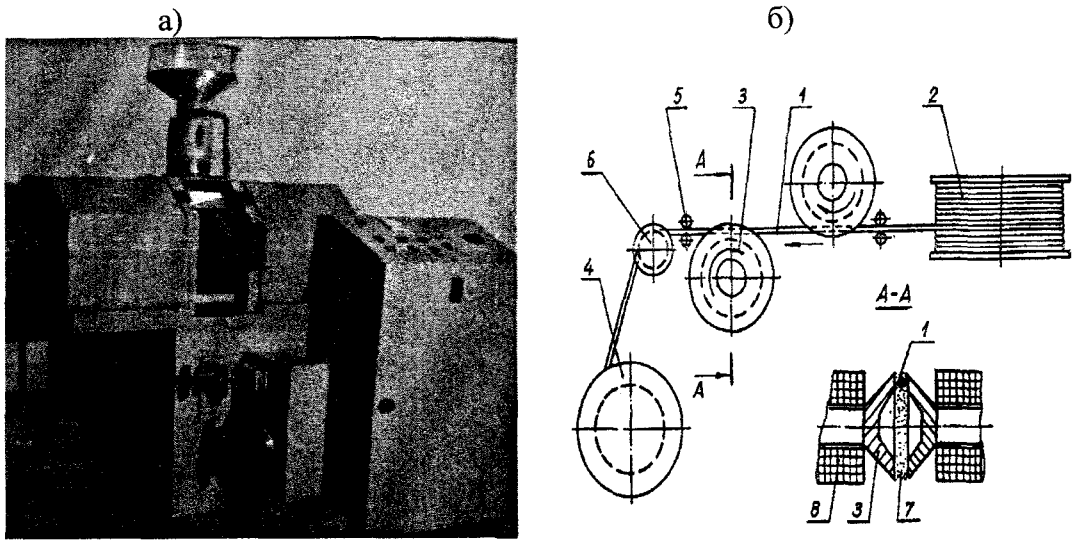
Общий вид (а) и схема работы (б) станка СФТ2.111:
